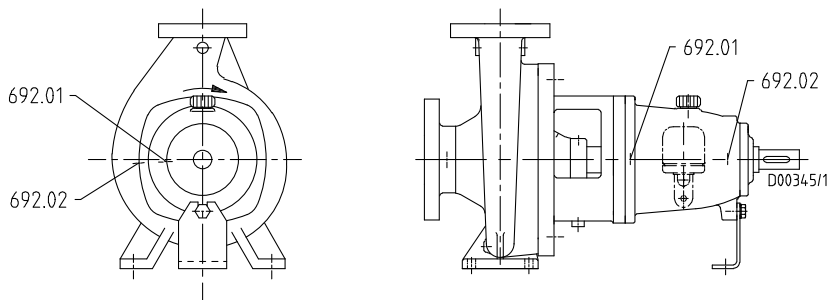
Присоединения СРКН, НРК: корпус подшипника UP03-UP06/P03s-P06s
